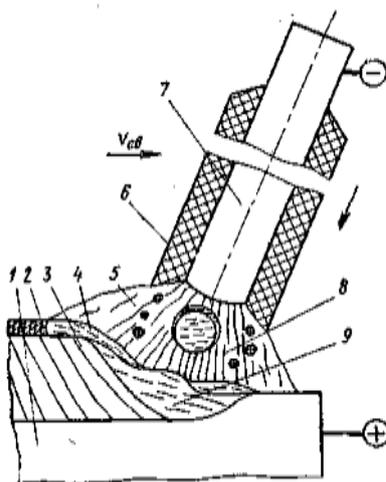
Схема процесса ручной дуговой сварки металлическим покрытым электродом
